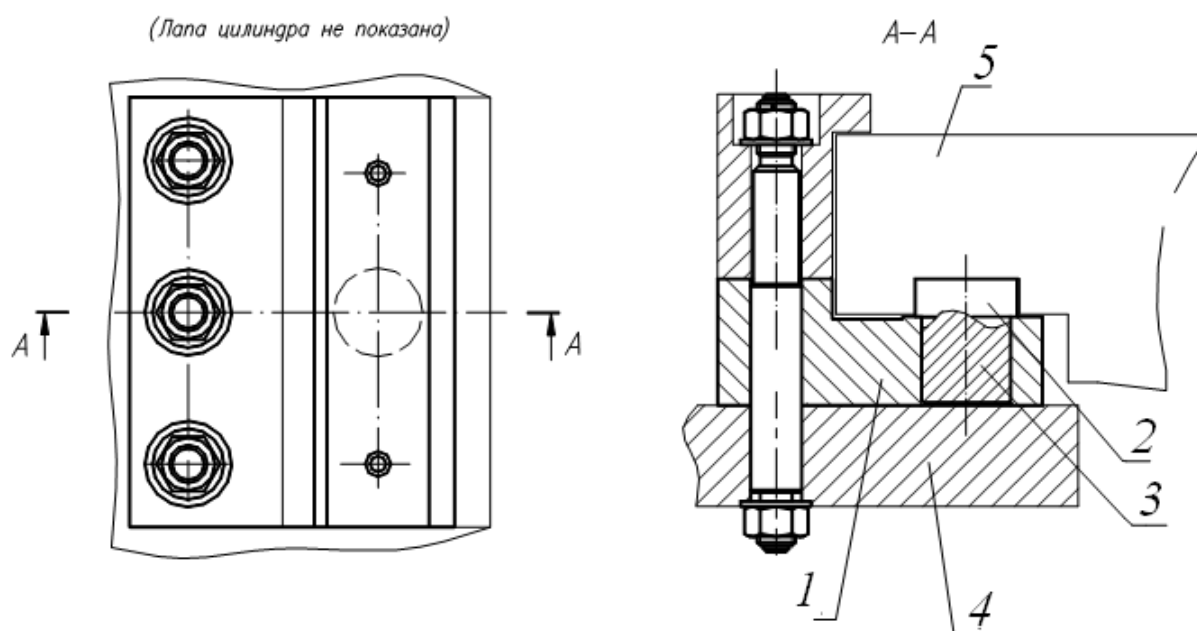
Конструктивная схема разрезной поперечной шпонки [48]
